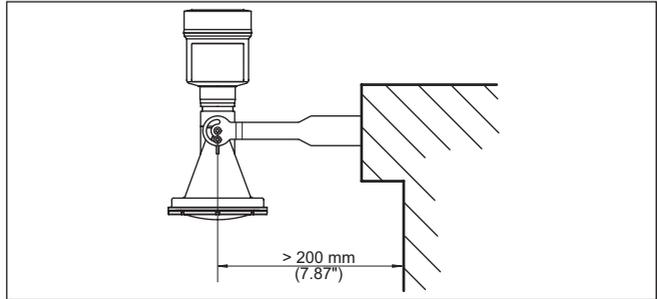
Montage mural horizontal via l'étrier de montage avec une longueur de 170 mm
